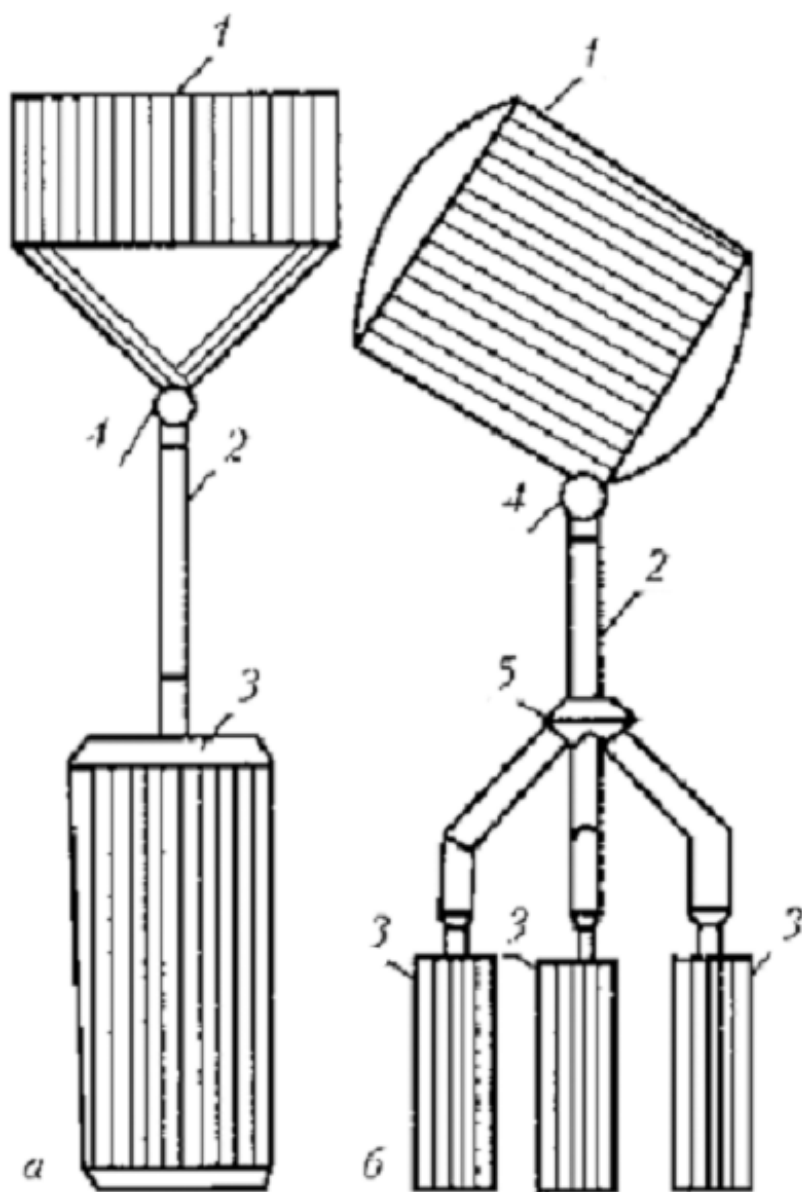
Схемы формующих установок для заполнения пресс-форм по способу свободного литья [15]:
